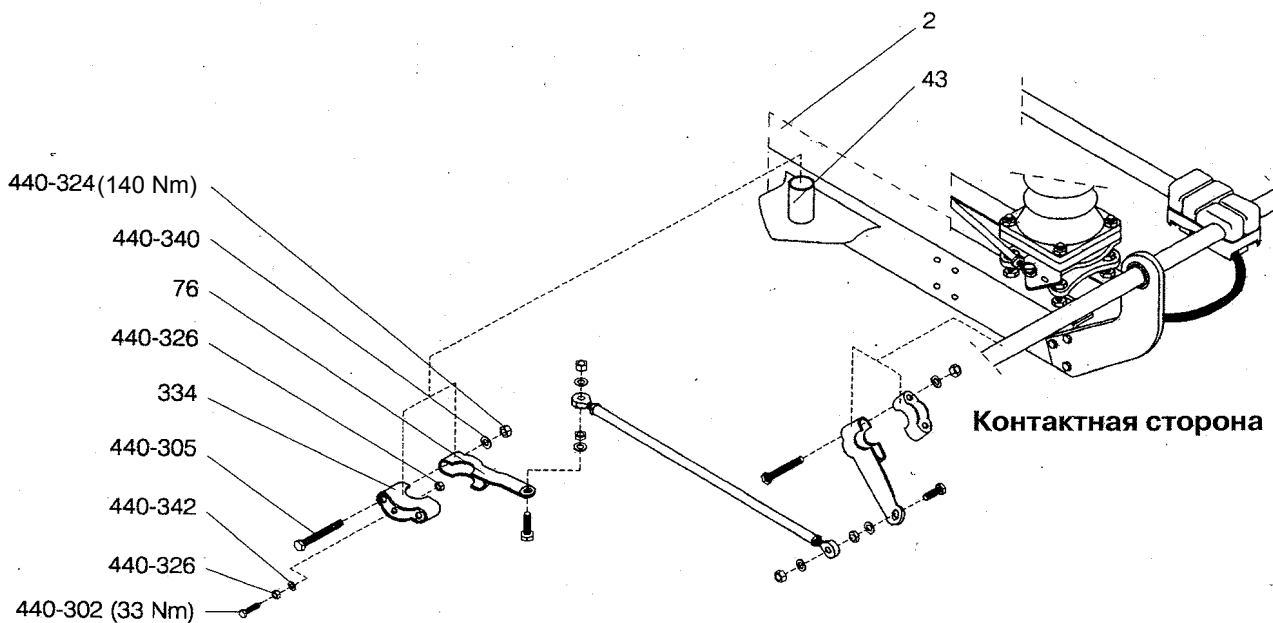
Установка приводного механизма заземлителя, монтаж на раме и раздельный монтаж. Установка приводного рычага (76) при расположении заземлителя на контактной стороне
